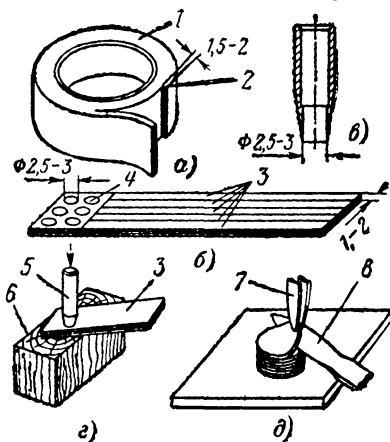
Заготовка кружков и полосок из липкой ленты.
